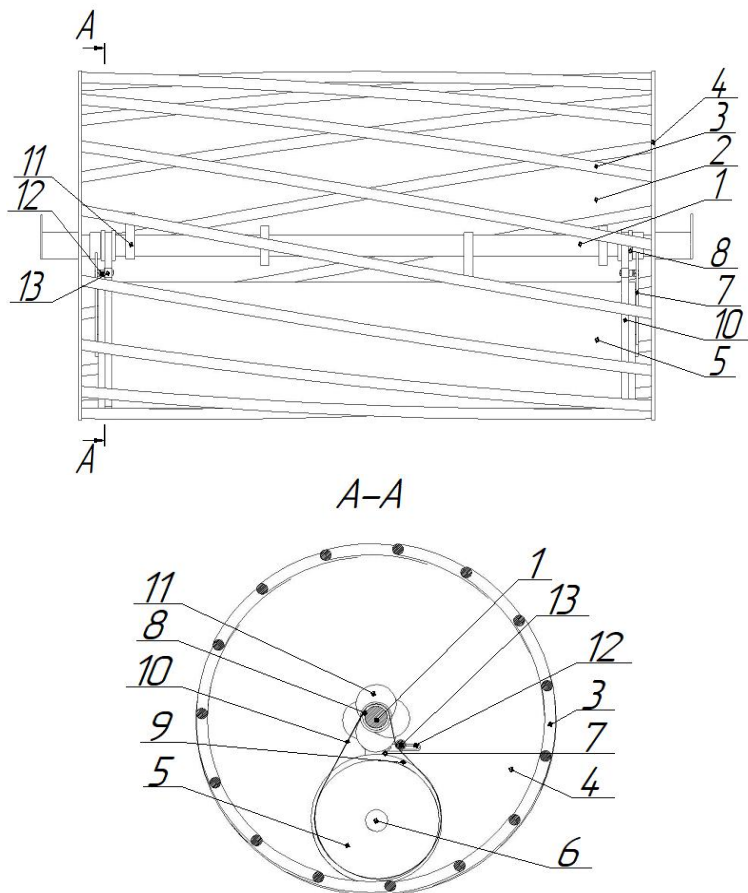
Почвообрабатывающий каток вибрационного действия: 1 - ось; 2 - пустотелый цилиндр; 3 - ребра; 4 - диски; 5 - гладкий цилиндр; 6 - ось гладкого цилиндра; 7 - поводки; 8 - шкивы; 9 - канавки; 10 - ремни; 11 - дебалансы; 12 - Z-образные кронштейны; 13 - ролики.
